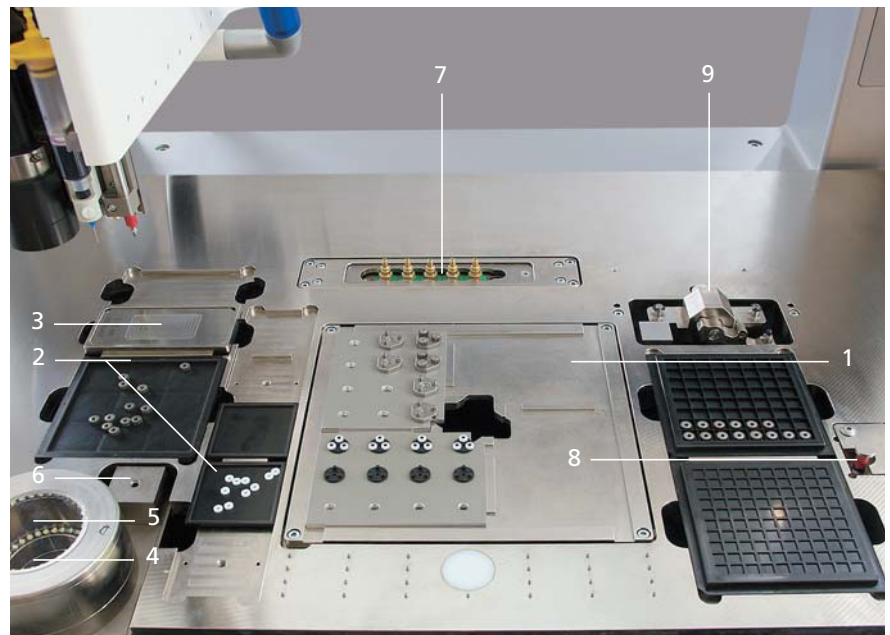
PLATE-FORME DE MONTAGE SUR TABLE DE MACHINE ONYX 32
